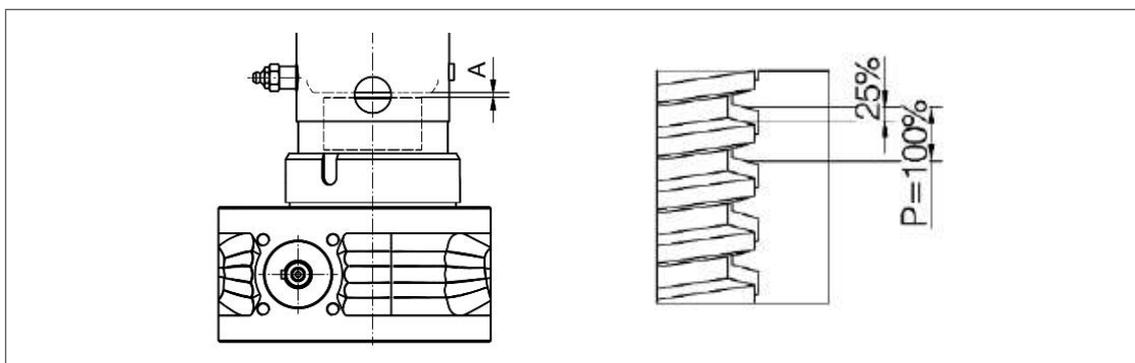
Chiocciola di sicurezza SIFA: dimensione „A“ per il confronto durante il test di usura
